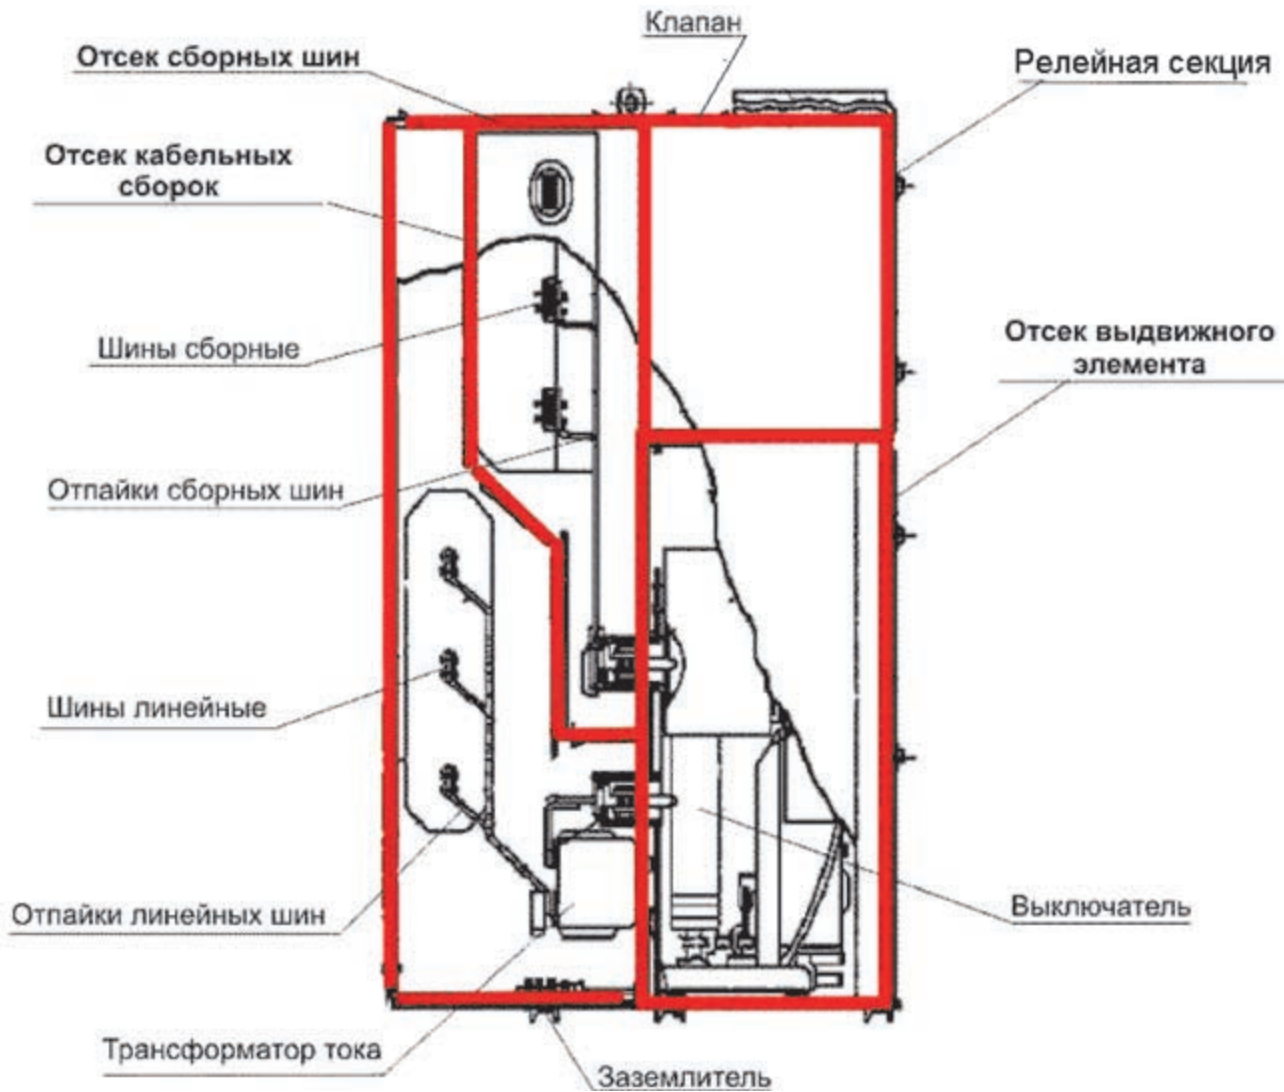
Компоновка шкафов с линейными шинами и выключателем на номинальные токи 630, 1000, 1600 А.
